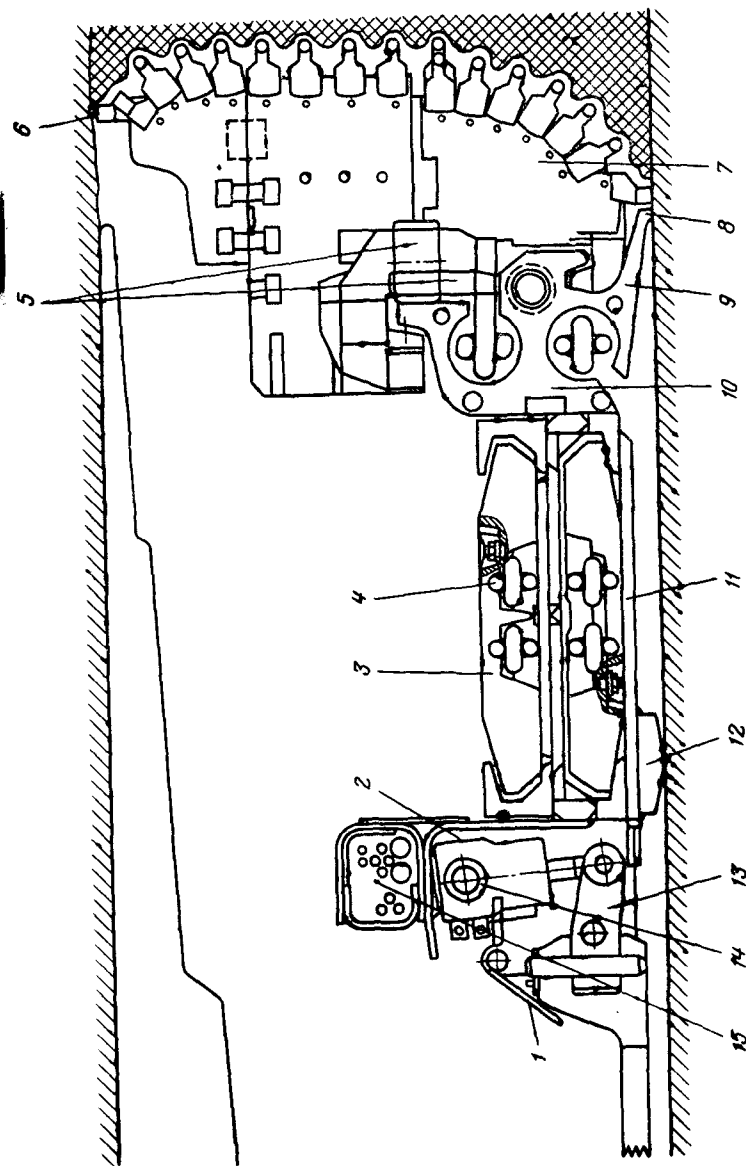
Компактный струг КНС 2: 1 — система индикации; 2 — навесной борт; 3 — скребок; 4 — скребковая цепь; 5 — ролики; 6 — резец; 7 — режущий башмак; 8 — скребковая опора; 9 — погрузочный полок; 10 — направляющая струга; 11 — желоб конвейера; 12 — поворотная опора; 13 — карданный механизм; 14 — цилиндр; 15 — кабельный канал
